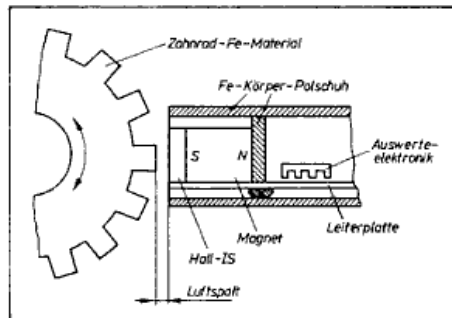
Zähne-Zahnrad-Sensor mit B 467 GE
